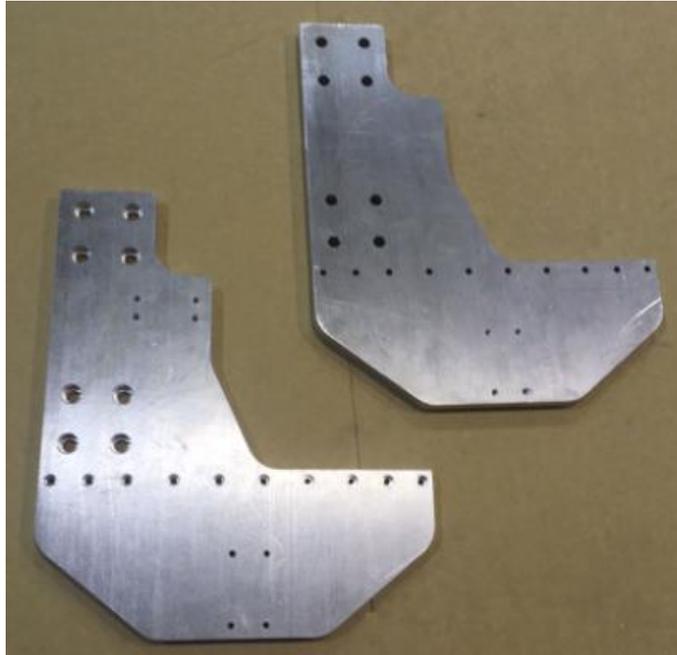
Placas laterales de aluminio 6061 T6 mecanizadas por CNC
